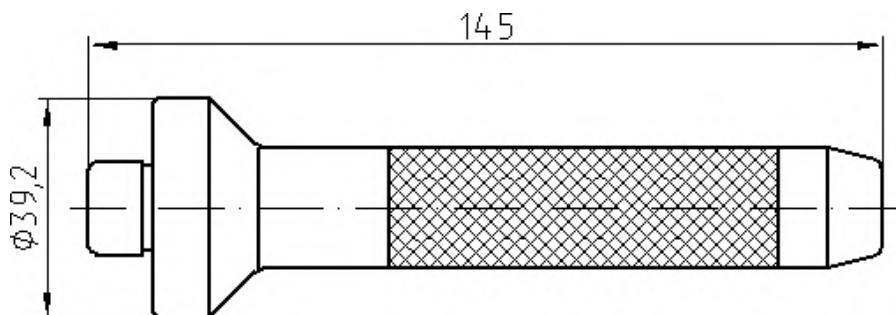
5-U-10897 – Spannvorrichtung zum Ein- und Auspressen des Lagers der Primärwelle des Getriebes
